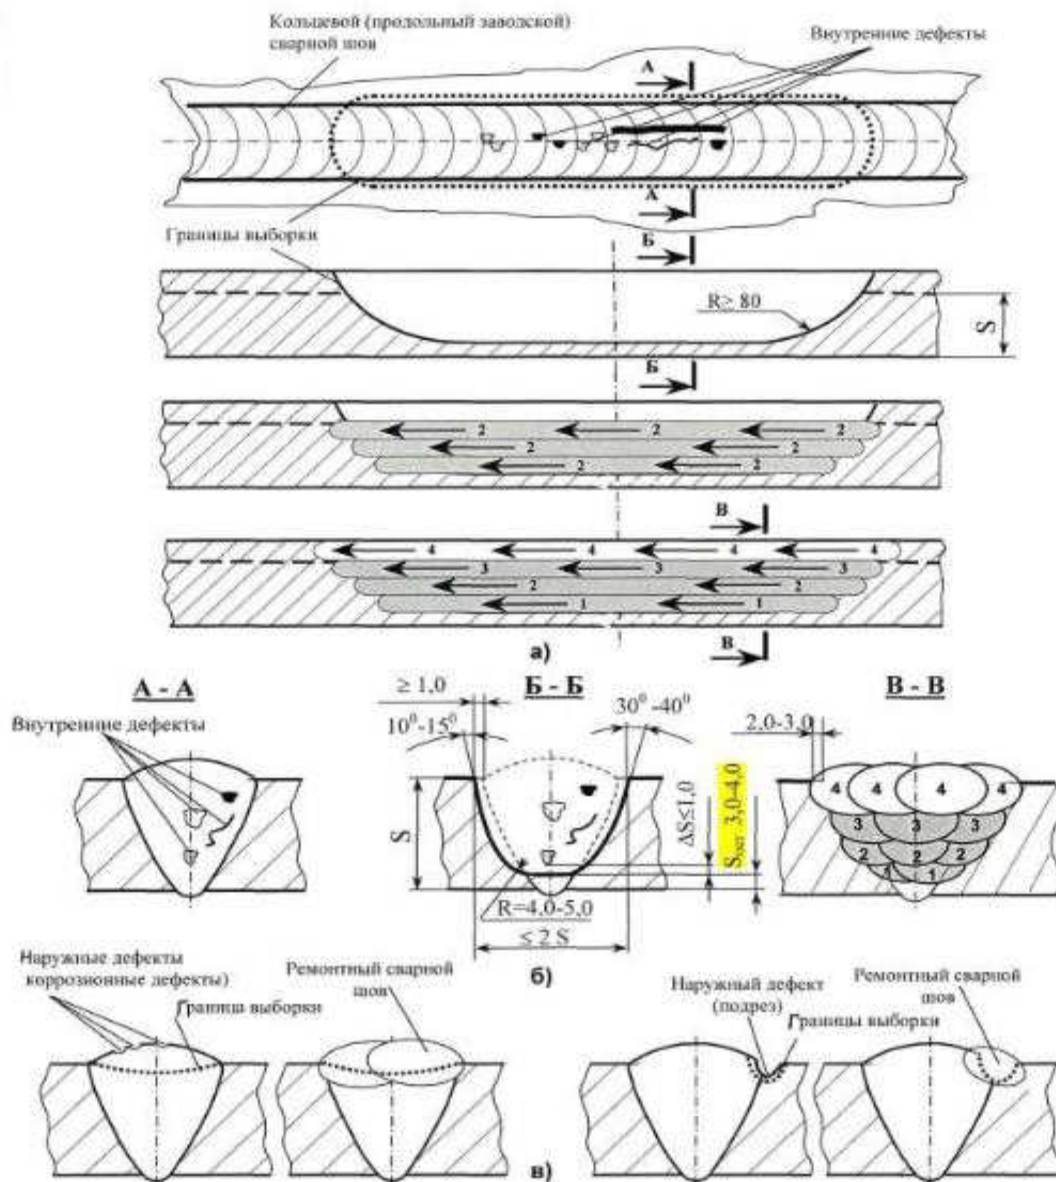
Параметры выборки дефектного участка, последовательность и направление слоев шва, параметры сварного шва при сварке (заварке) несквозной выборки прямолинейной формы длиной до 150 мм (выборка и сварка за один этап)
